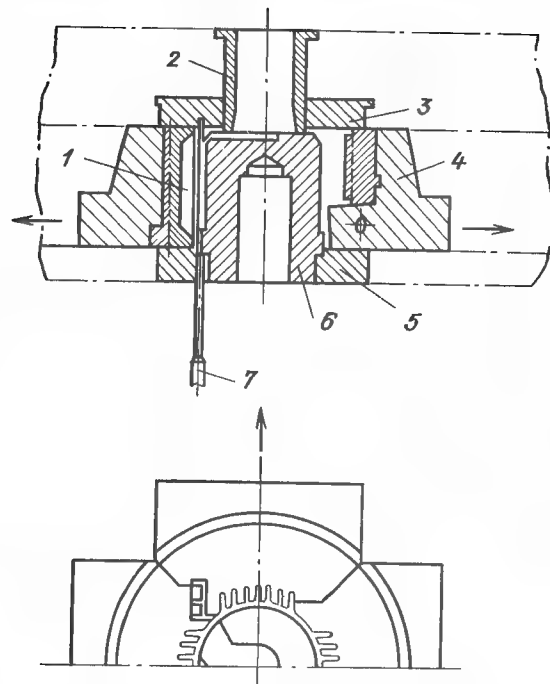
Четырехсекторная пресс-форма для отливки из высокопрочного алюминиевого сплава станин с вертикально-горизонтальным оребрением:
